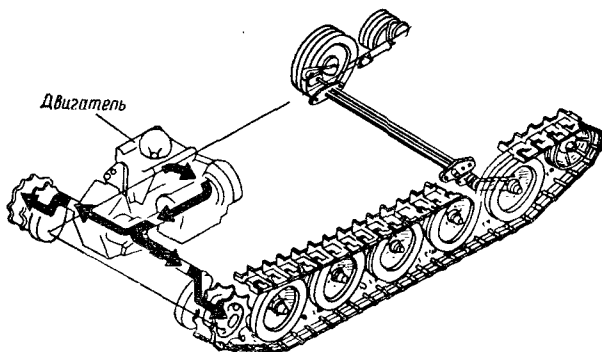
Схема расположения основных агрегатов на плавающем гусеничном бронетранспортере М-113
